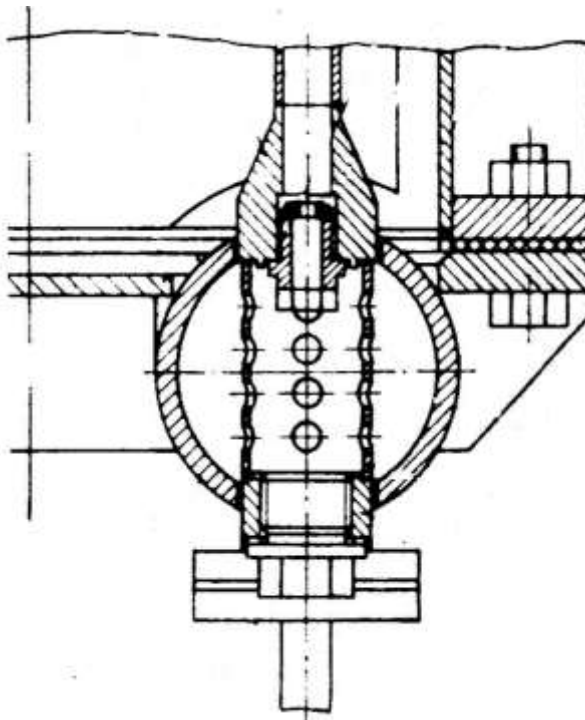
Сварные соединения в котлах типа КУП
